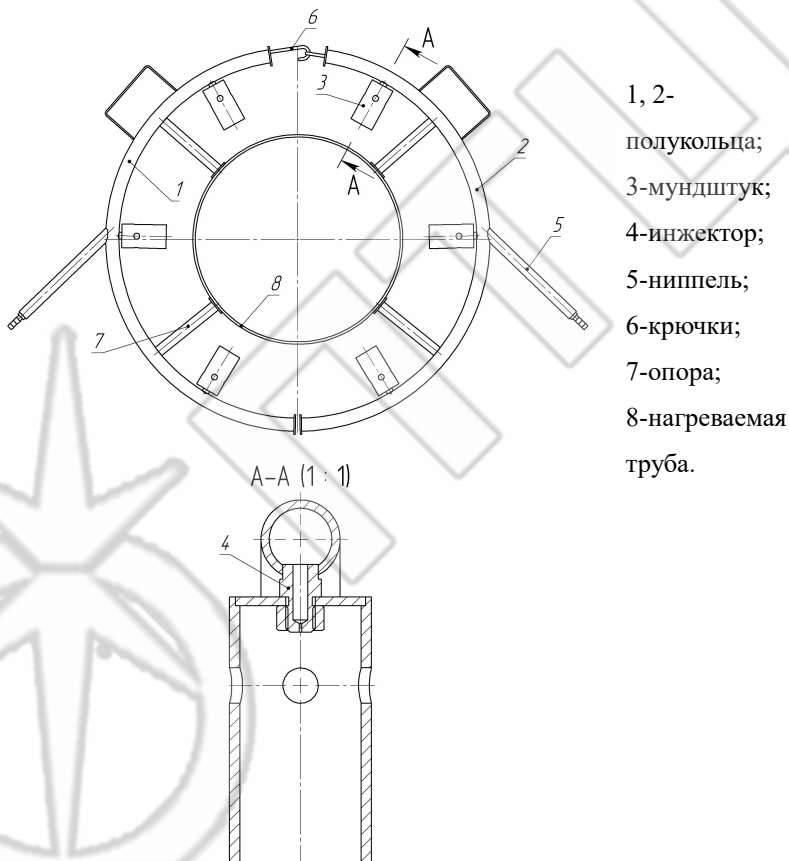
Горелка воздушная многопламенная для подогрева стыков труб ПСТВМ-Д "СФЕРА"
